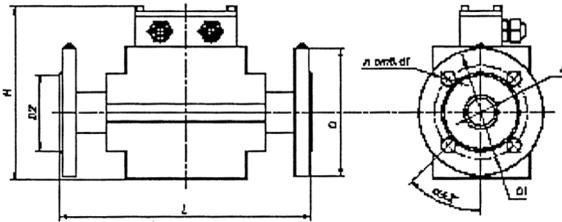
Габаритные и установочные размеры ПРПЭ типа ПРЭ 02
